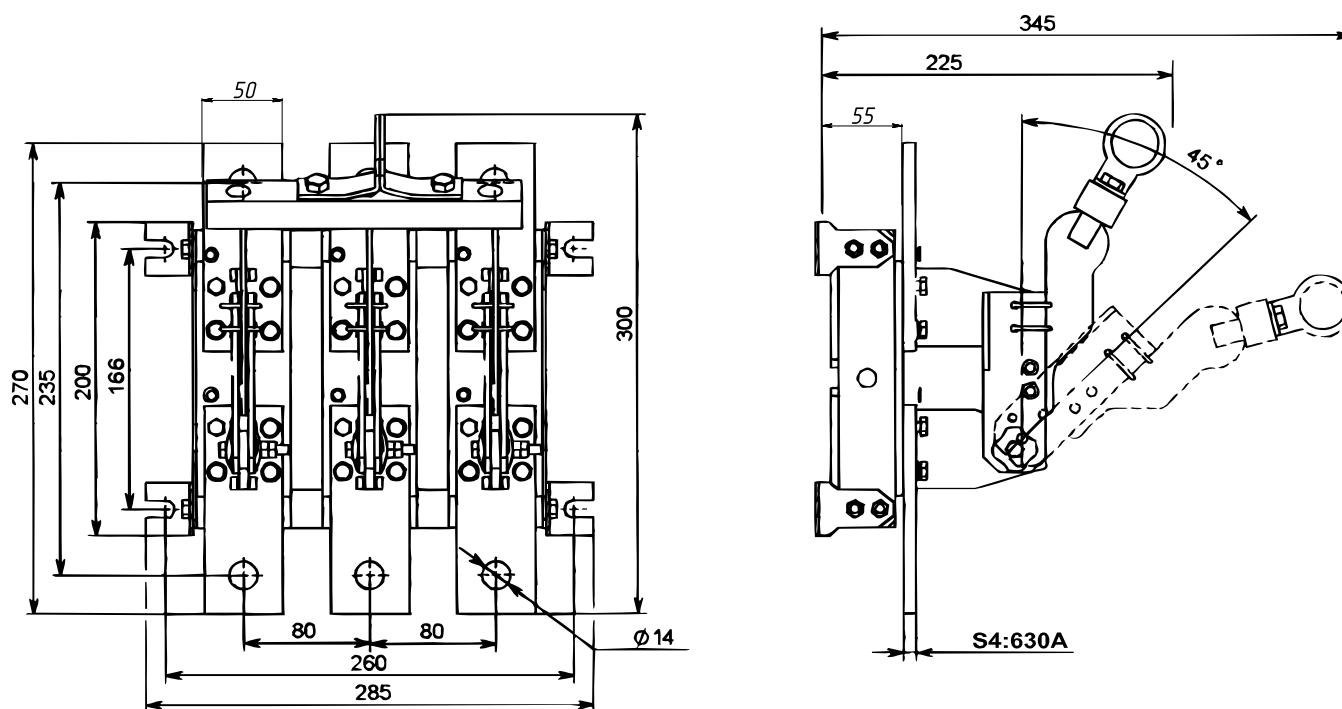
Разъединитель PE19-39-31190-00 УХЛЗ с центральным рычагом для управления штангой
